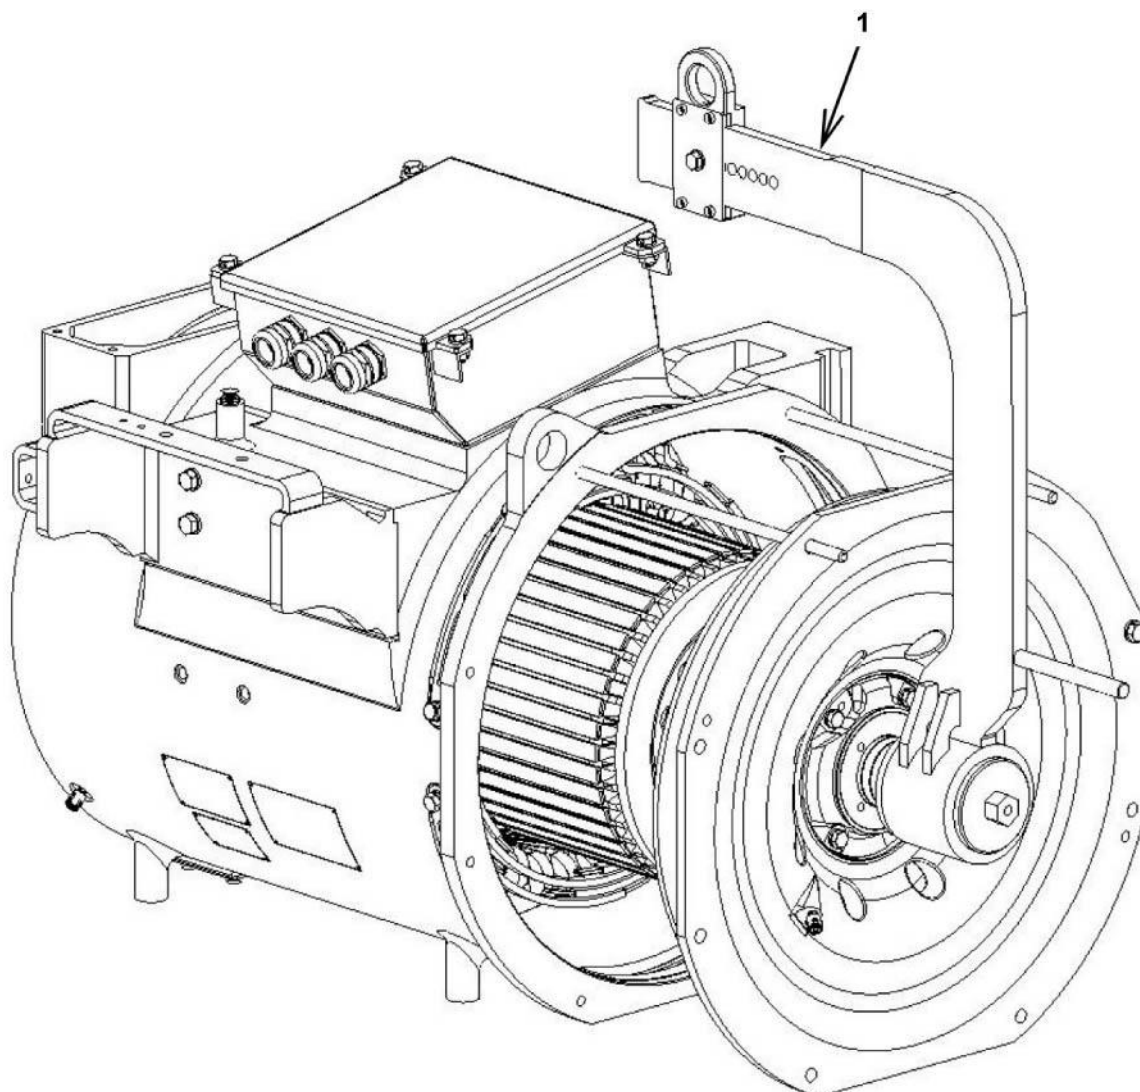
Ferramenta especial para instalação do conjunto do rotor.
